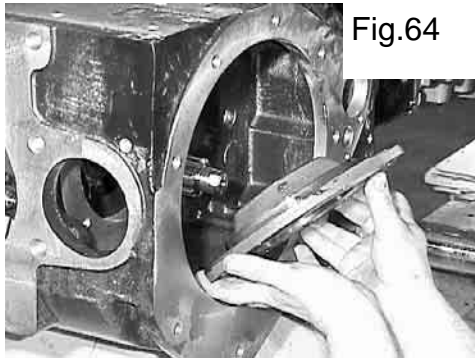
Après quoi on pourra continuer avec le montage, en terminant la partie arrière de la machine, c'est-à-dire en préparant le culot arrière de fermeture dans laquelle sont logés les engrenages de commande et la sélection de la prise de force arrière.
